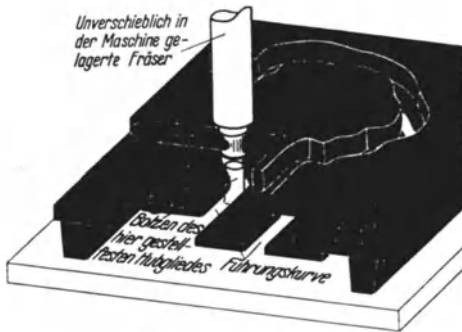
Gestaltunggebender Kurventrieb für Holzbearbeitung. (Werkstück aufgespannt auf einem Führungsbrett mit Führungskurve. Führungsbolzen im Gestell genau unter dem Holzfräser.)
